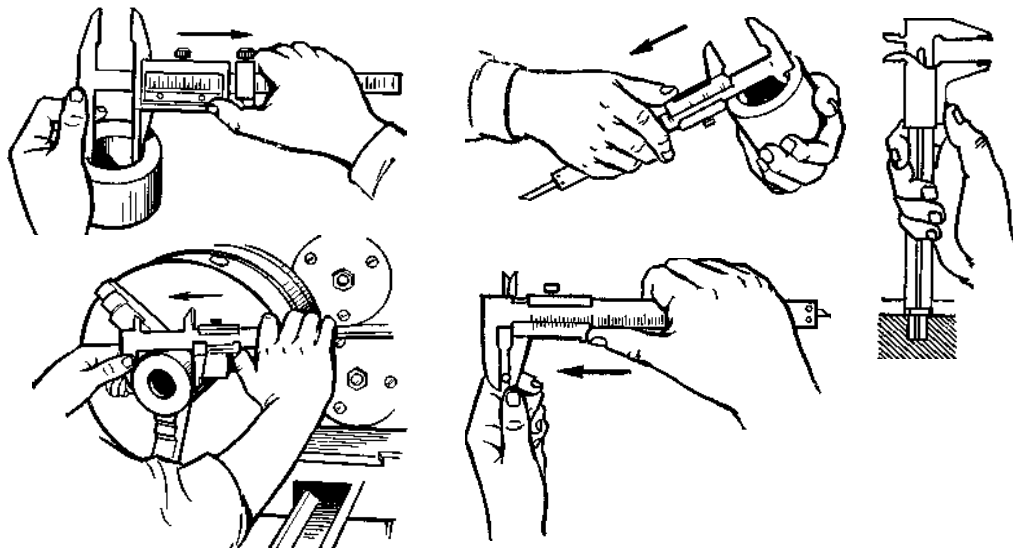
Основні прийоми роботи зі штангенциркулями
